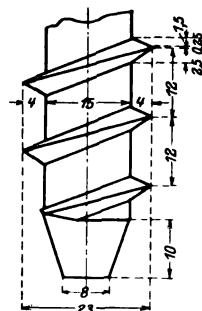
Gewinde der niederländischen Schwellenschraube.
